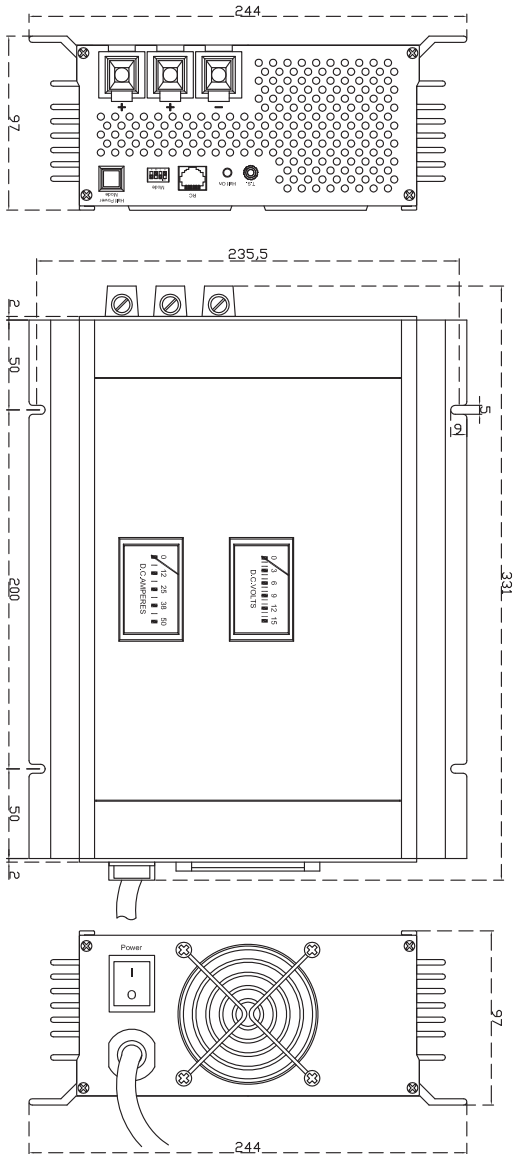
,1 Schéma dimensionnel des SEC-1250UL et SEC-2425UL
